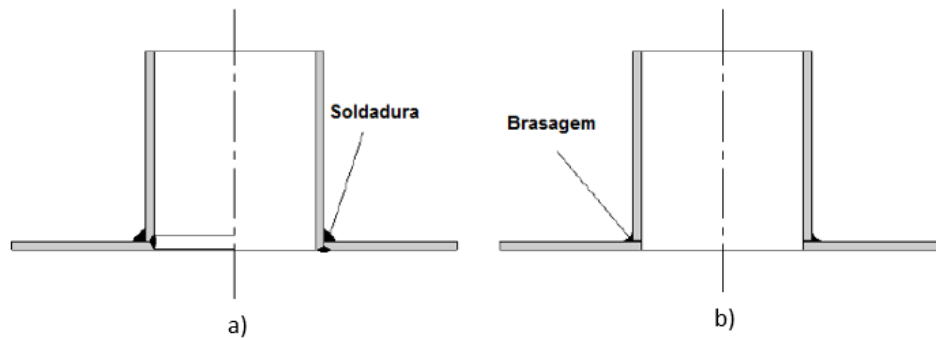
Processo convencional de ligação. a) Soldadura. b) Brasagem [7].
